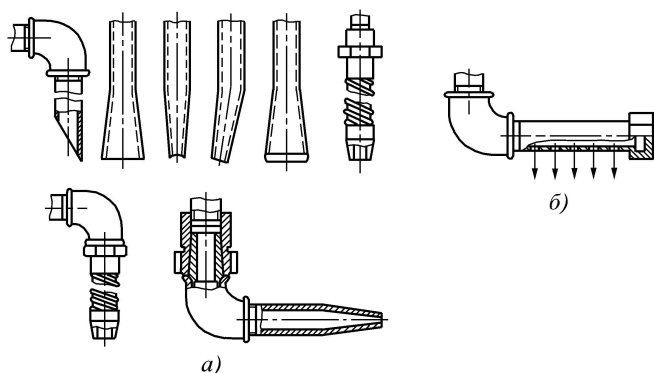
Сопловые насадки для подачи СОТС поливом:
